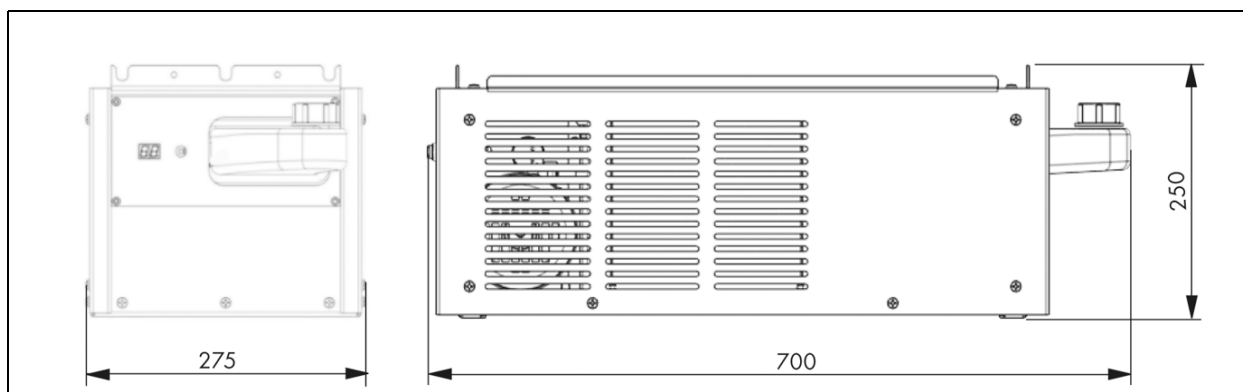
Dimensiones del recirculador de refrigerante iROB Cool
